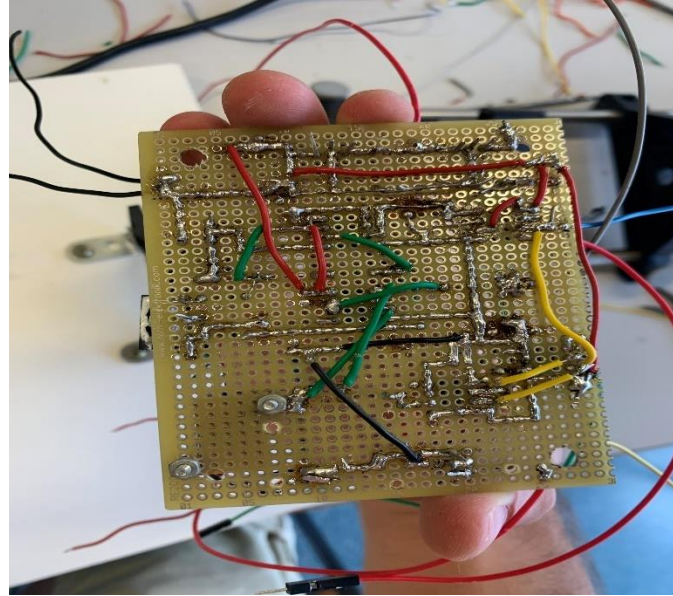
Vista de las soldaduras por la parte inferior de la placa
